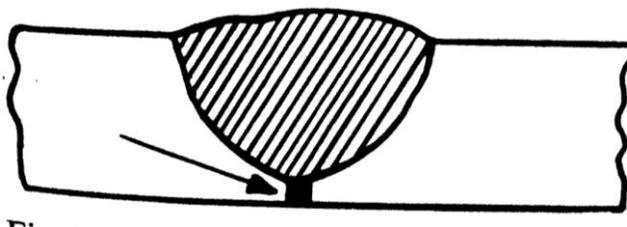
Aspecto de la falta de penetración en la soldadura (Rosario Francia, 2012)
